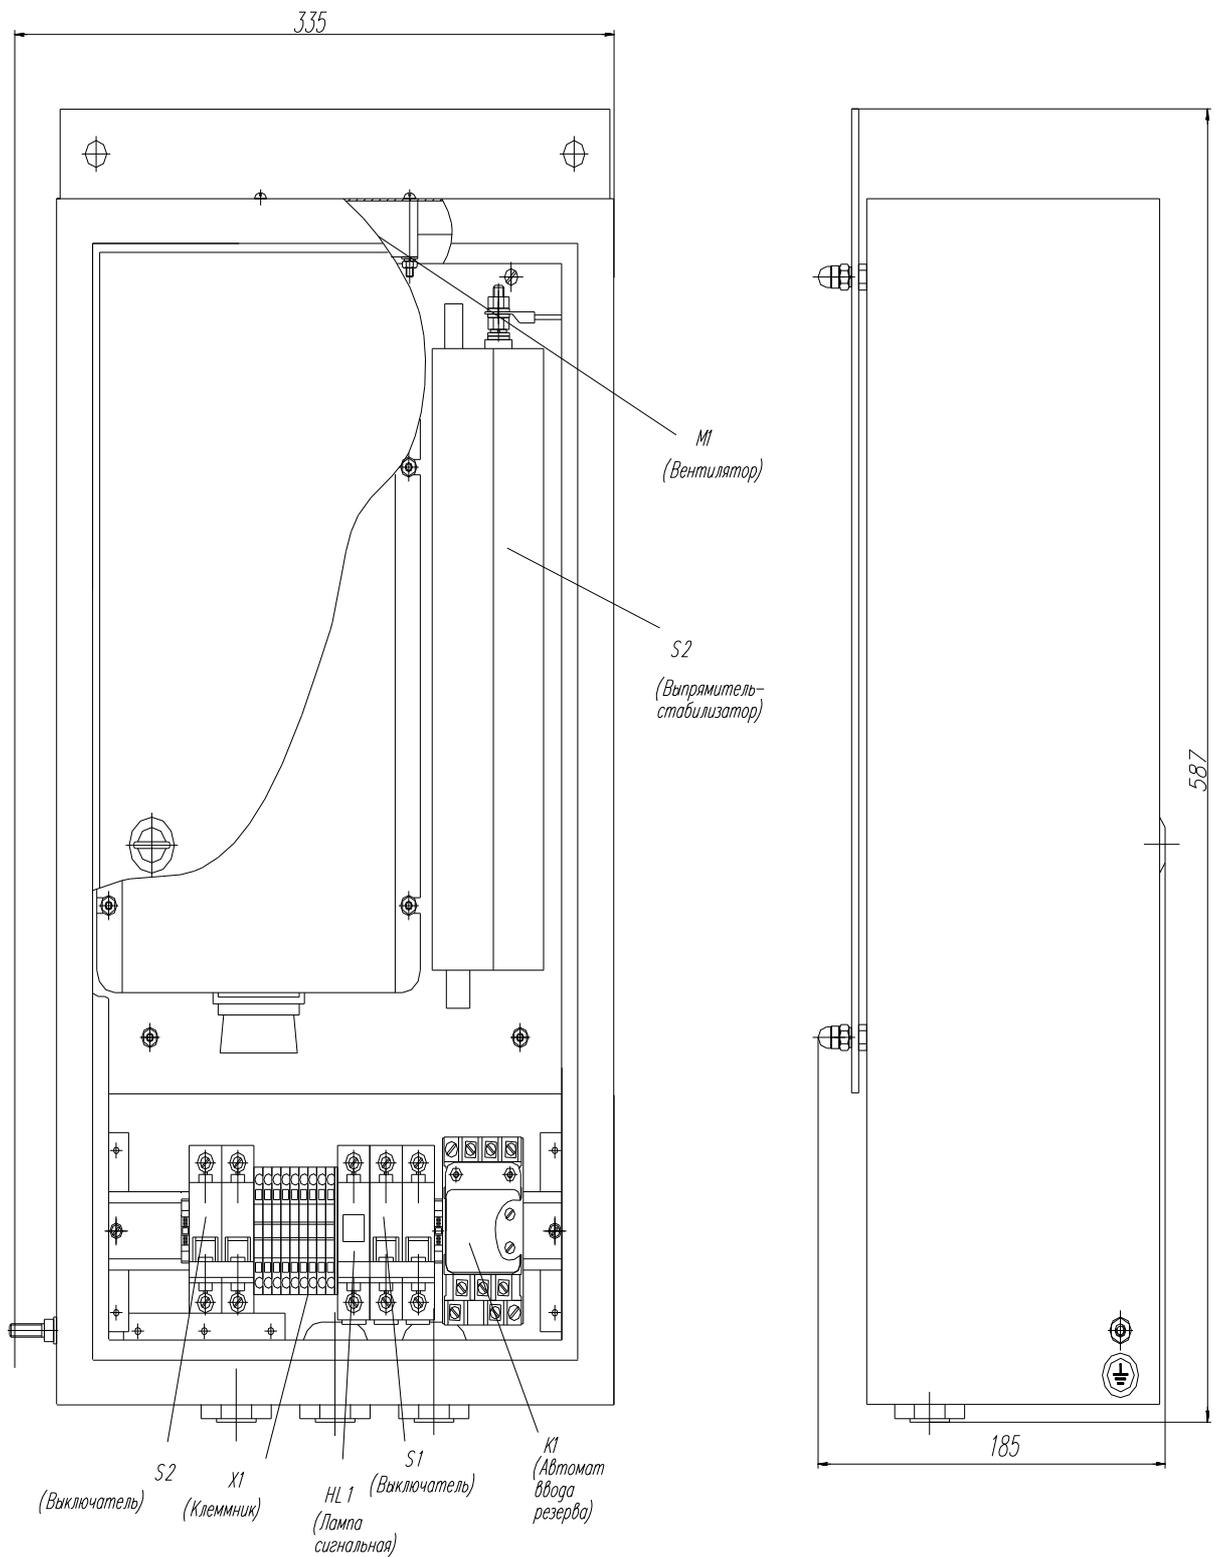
Габаритный чертеж и расположение элементов схемы БИ
